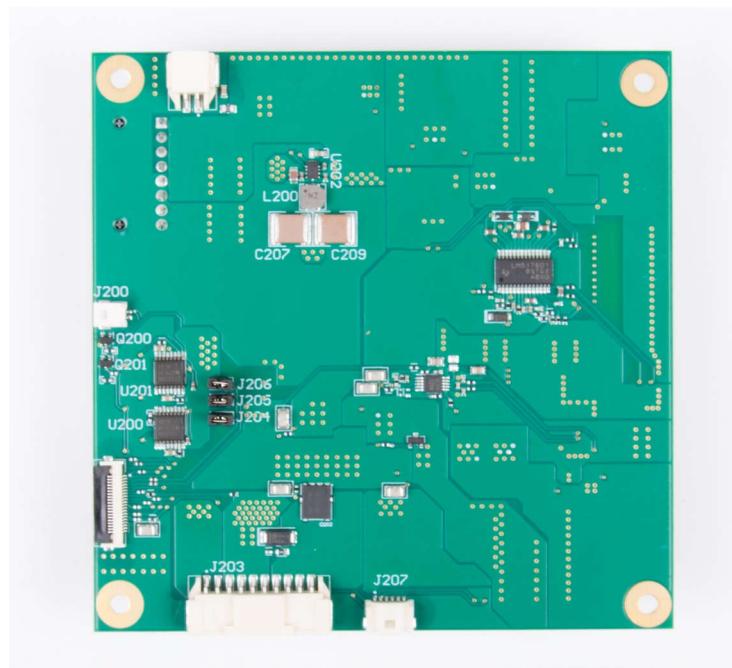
DLP5532PROJHBQ1EVM 照明ドライバ PCB (底面)
